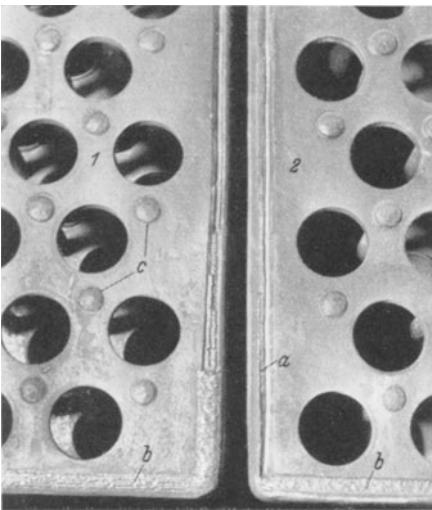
Geschweißte Umlaufbleche an einem Wasserkammerkessel.
